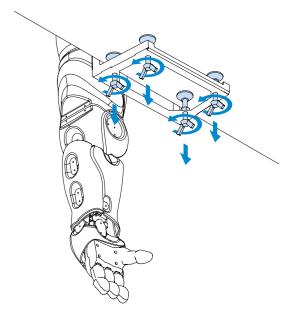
Демонтаж крепления Rooky с рабочей поверхности
